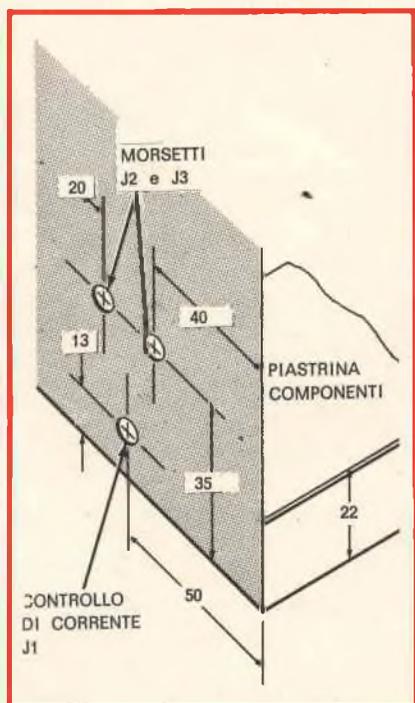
Disposizione dei morsetti e del connettore sul pannello.
